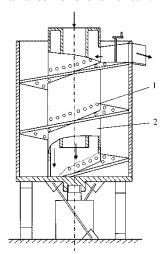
Подъемный винтовой вертикальный вибрационный СНД (патент РФ 2209109): 1 — ряд отверстий; 2- стенка загрузочного бункера
